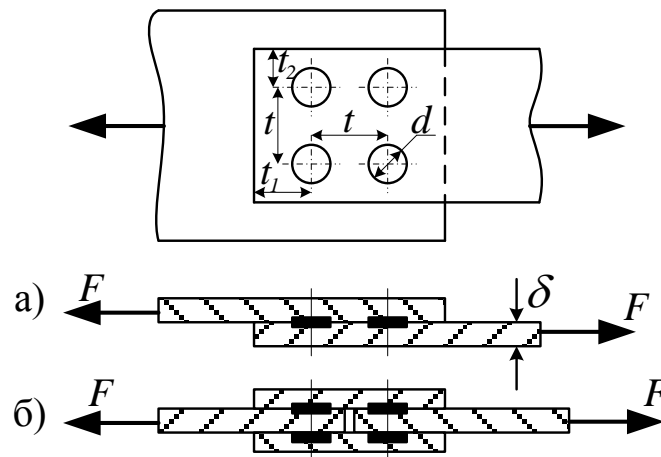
Расчетная схема соединения контактной сваркой
